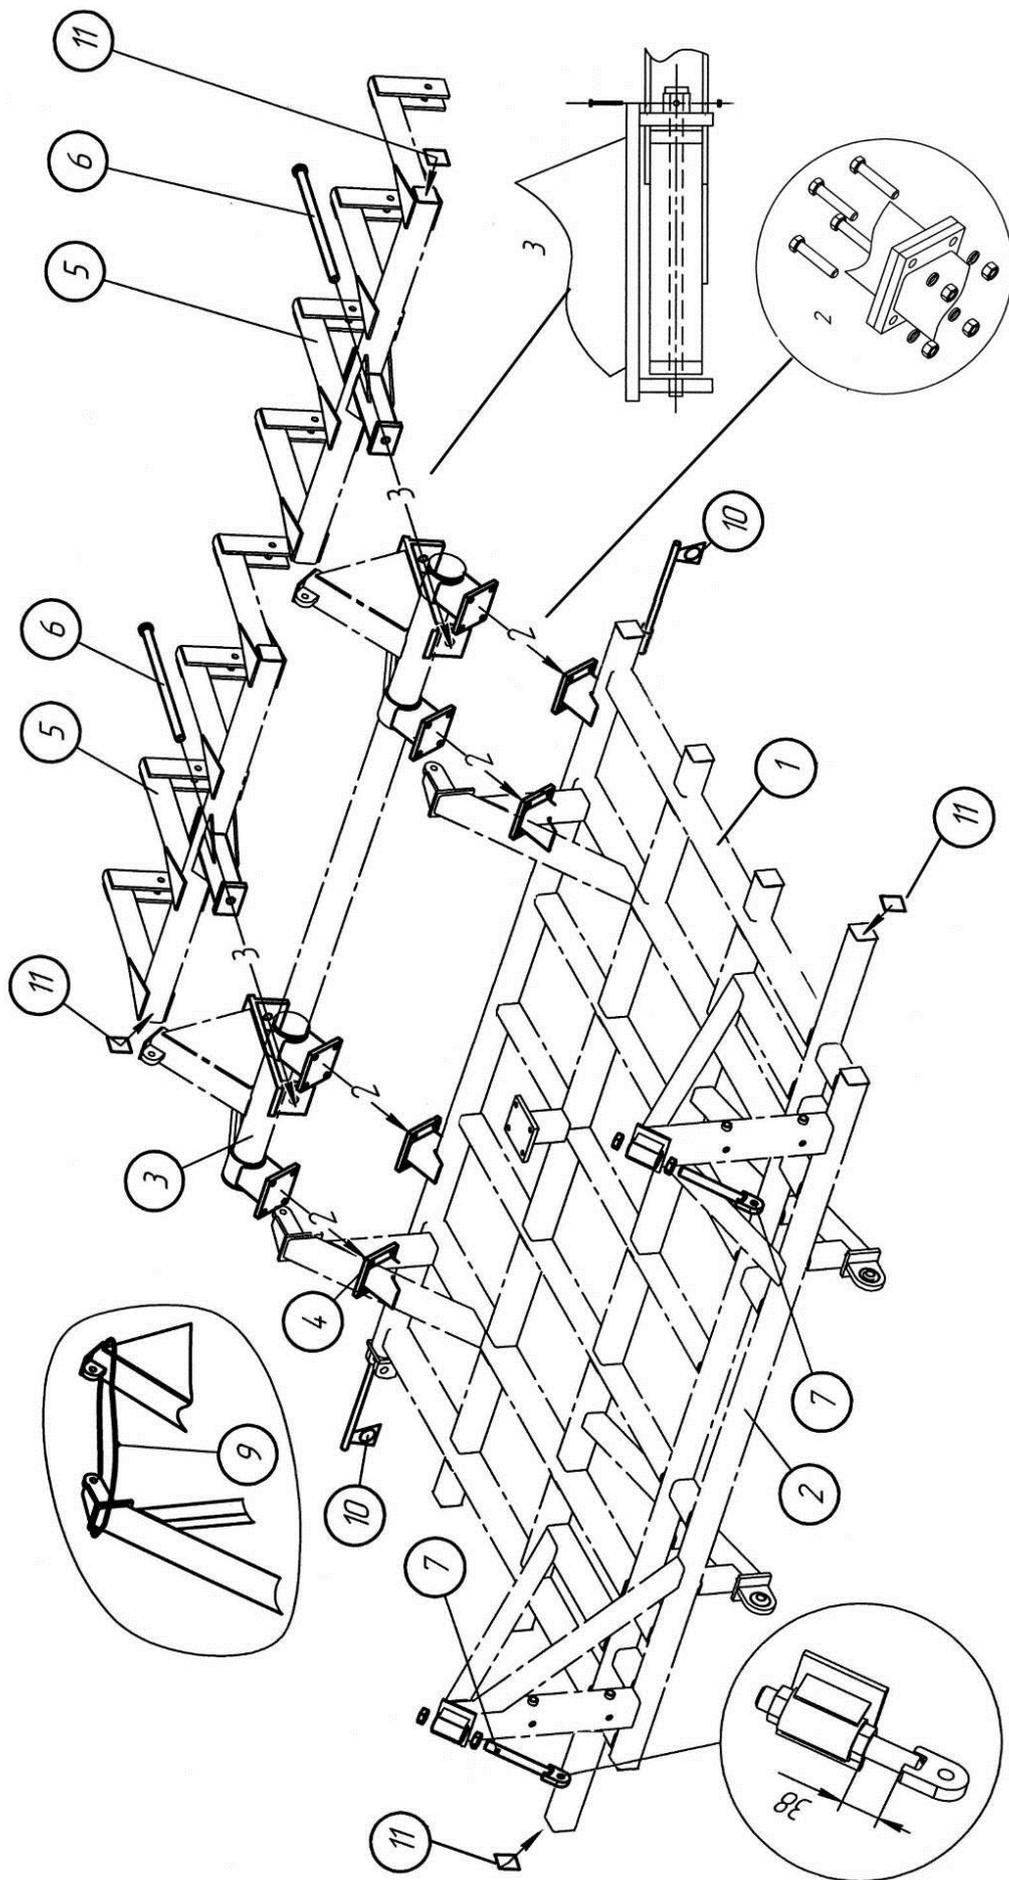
Сборка рамы, поворотного вала и подвески прикатывающих колес ПК-4,8Б
